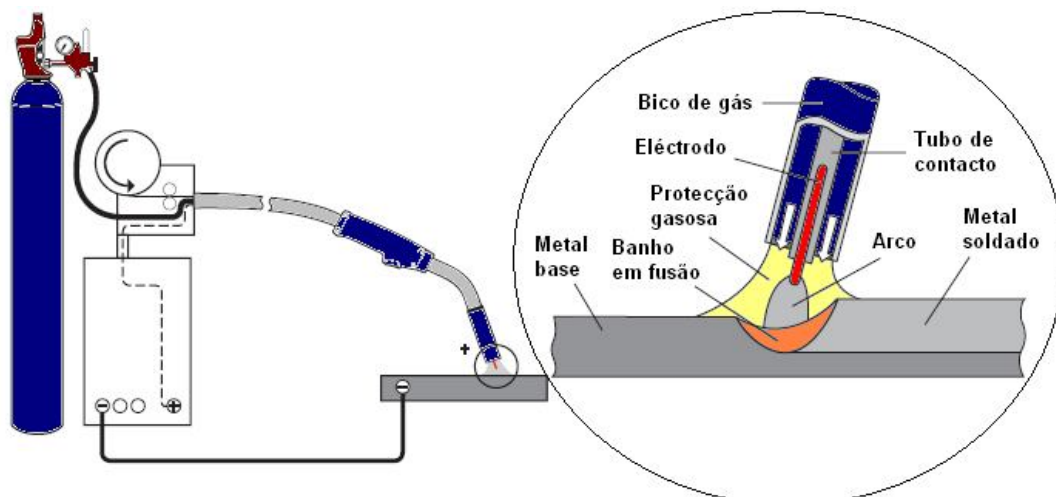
Esquema de uma soldadura MIG.
